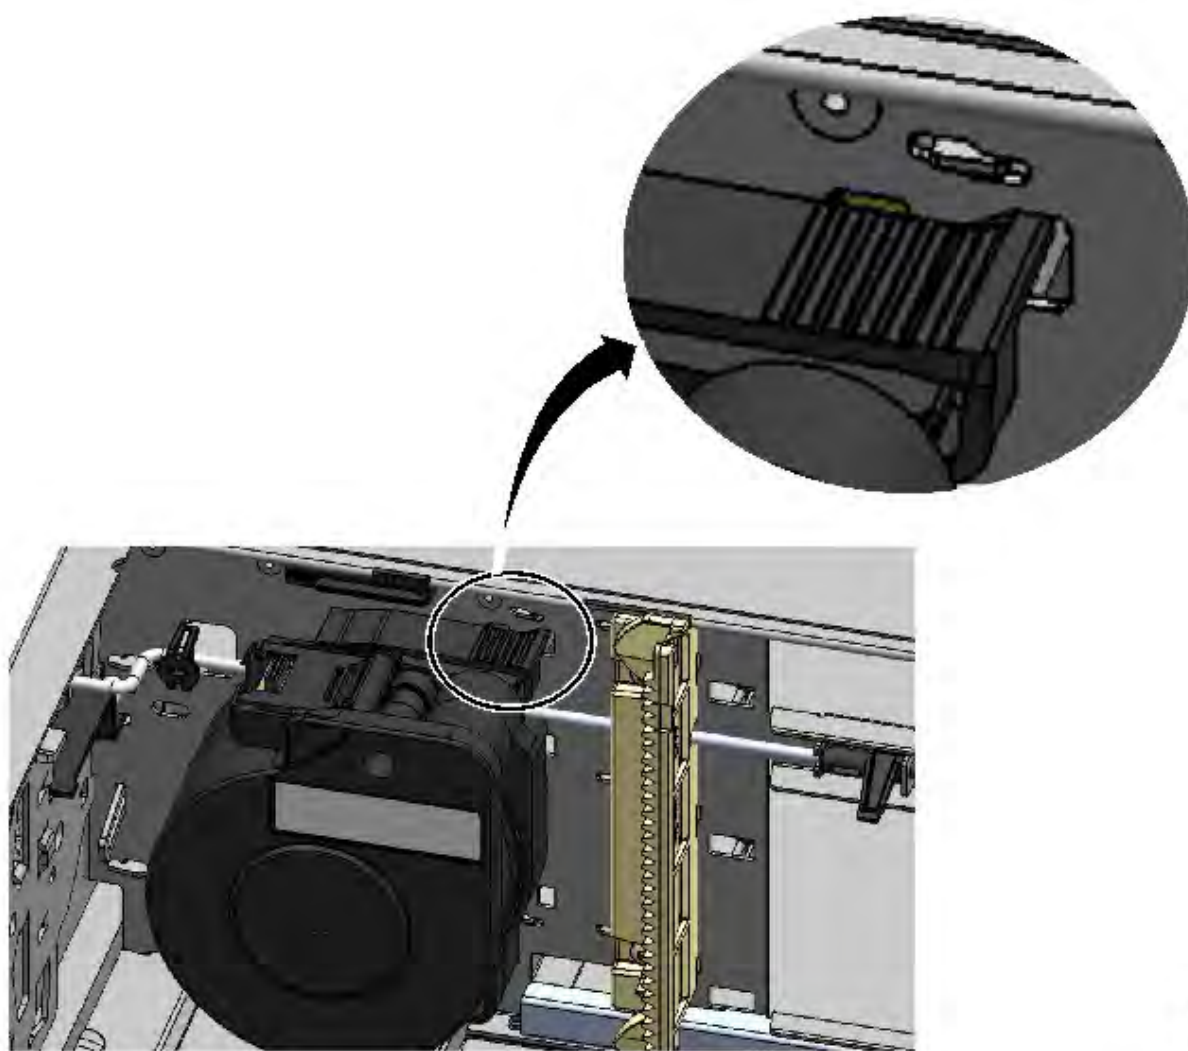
Mécanisme d'enroulement déverrouillé - vue agrandie
